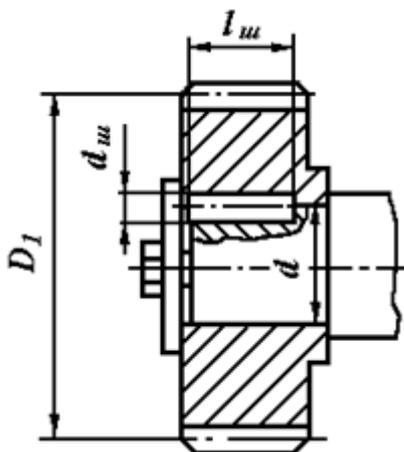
Шпоночное соединение зубчатого колеса с валом
